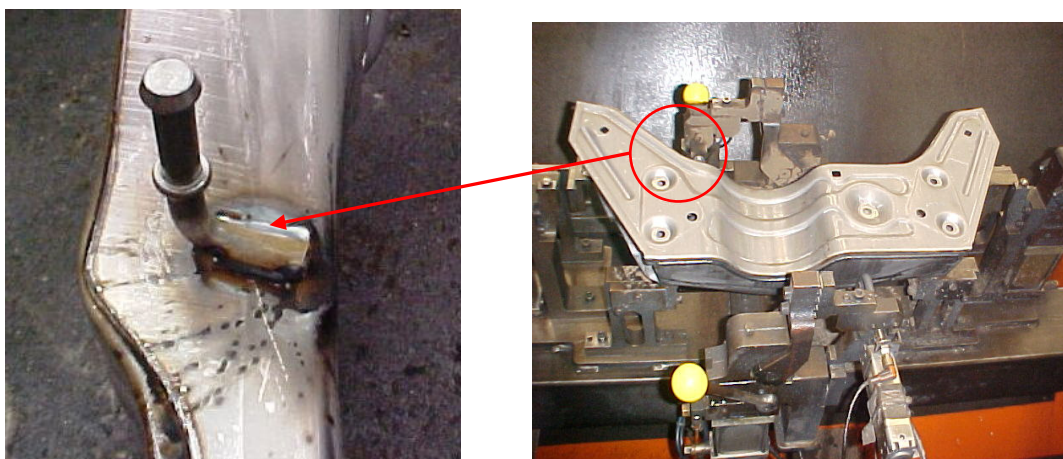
Dispositivo de solda com a peça posicionada (MIRON, 2007)
